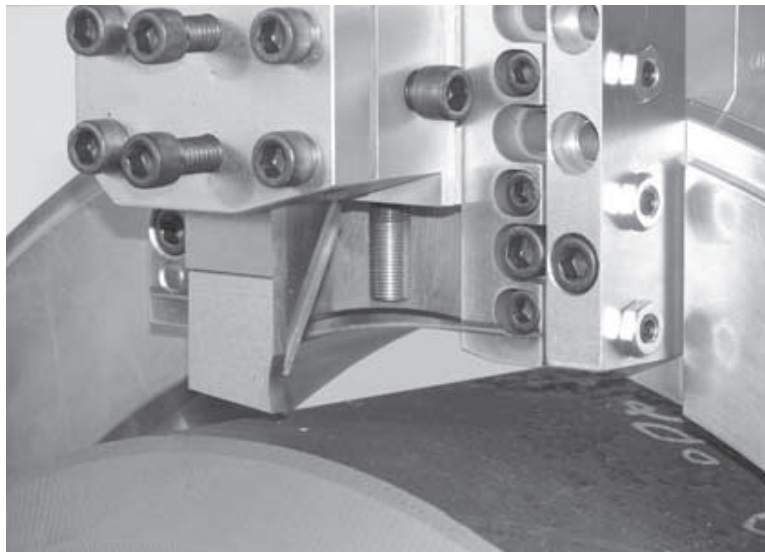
La foto muestra la herramienta de tronzado a 1/8" (3 mm) arriba de la marca.
